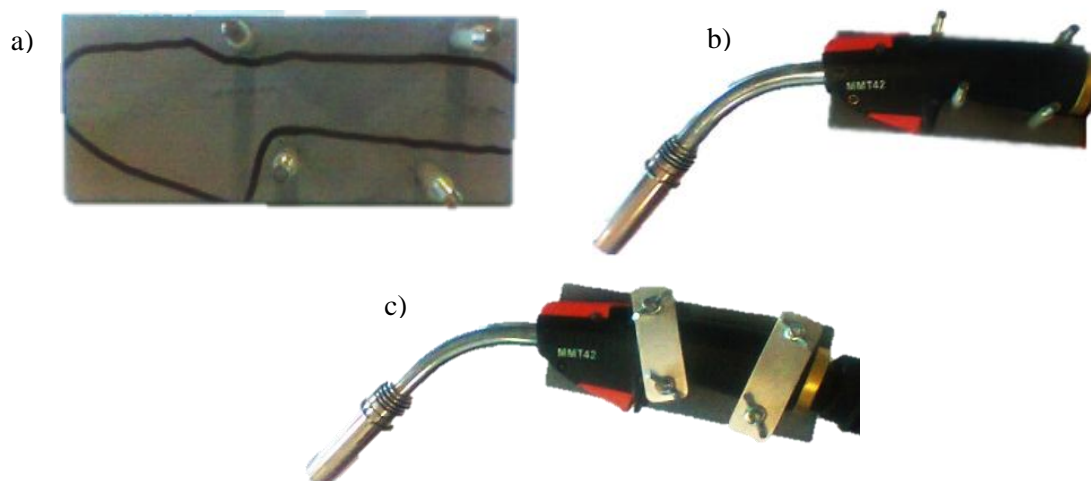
Montagem da tocha de soldadura no suporte
